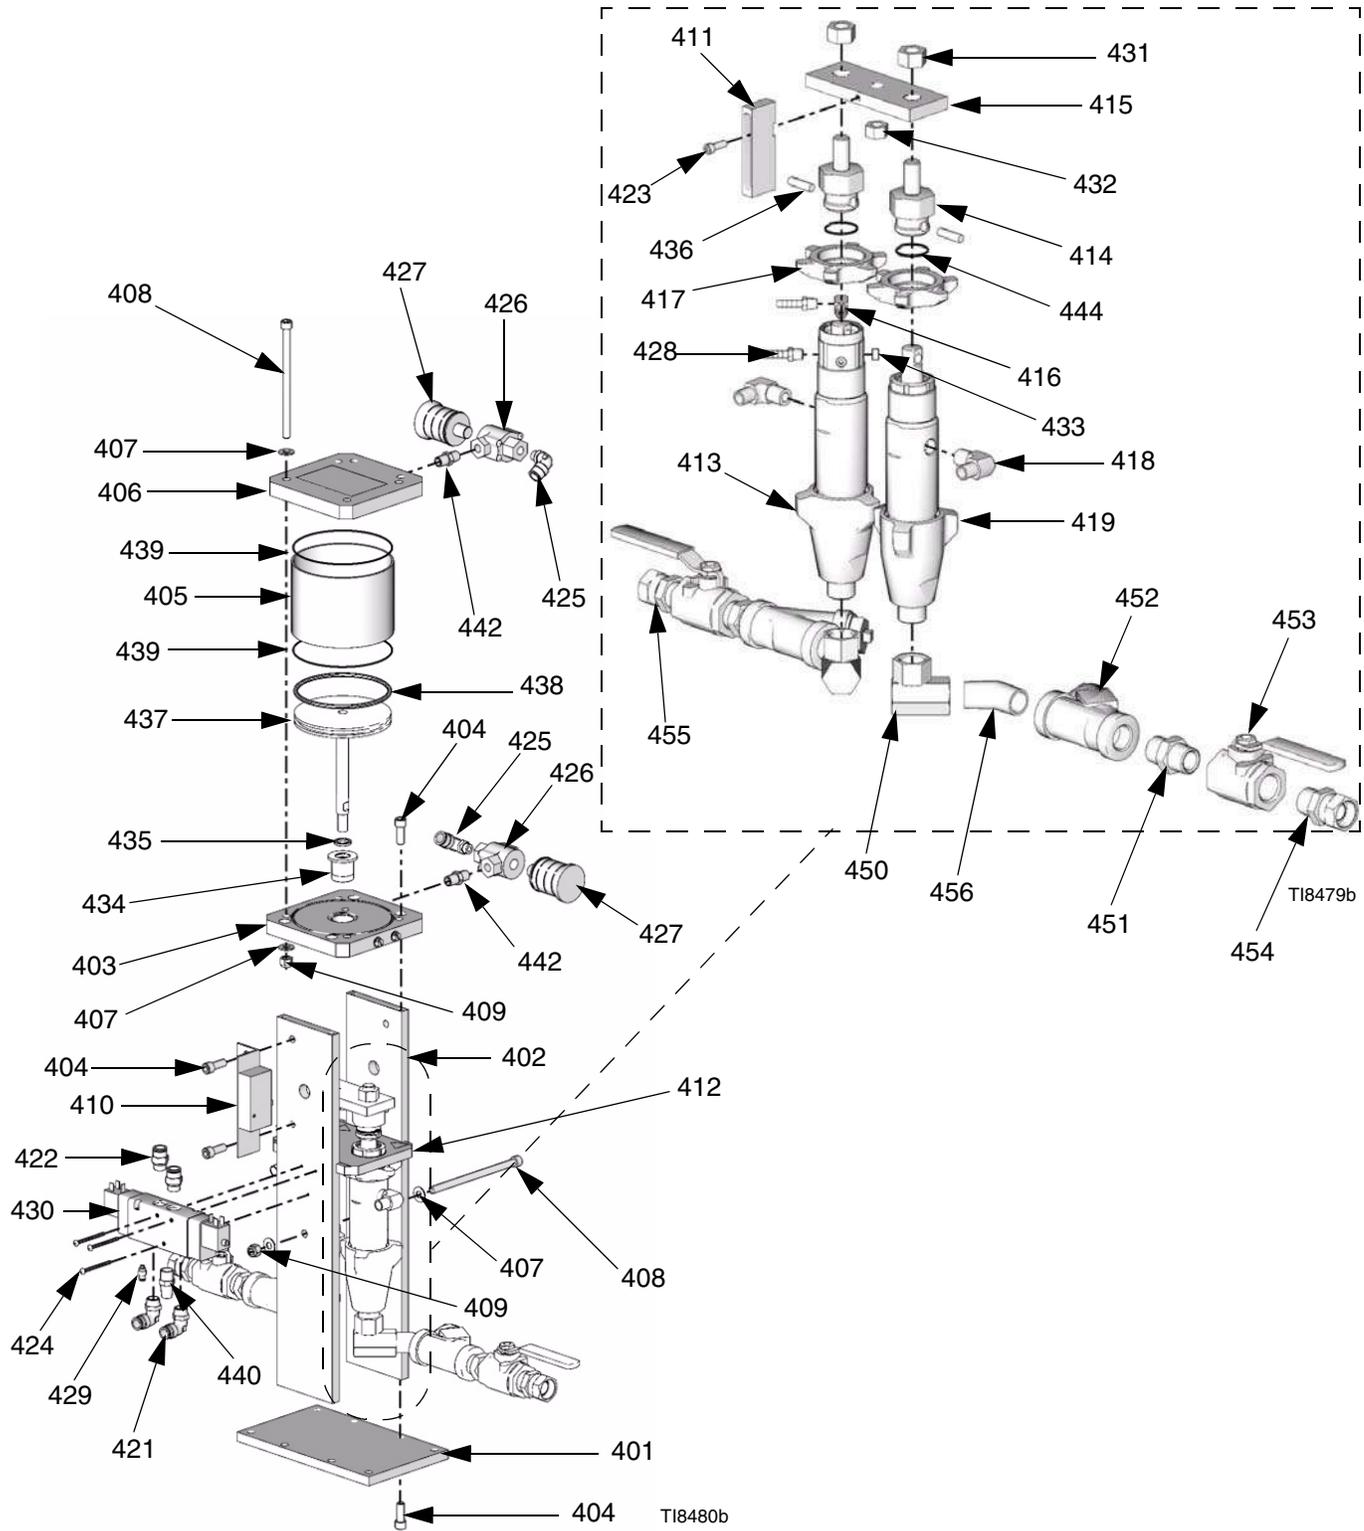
Ensemble de la pompe du moteur pneumatique du A-20
